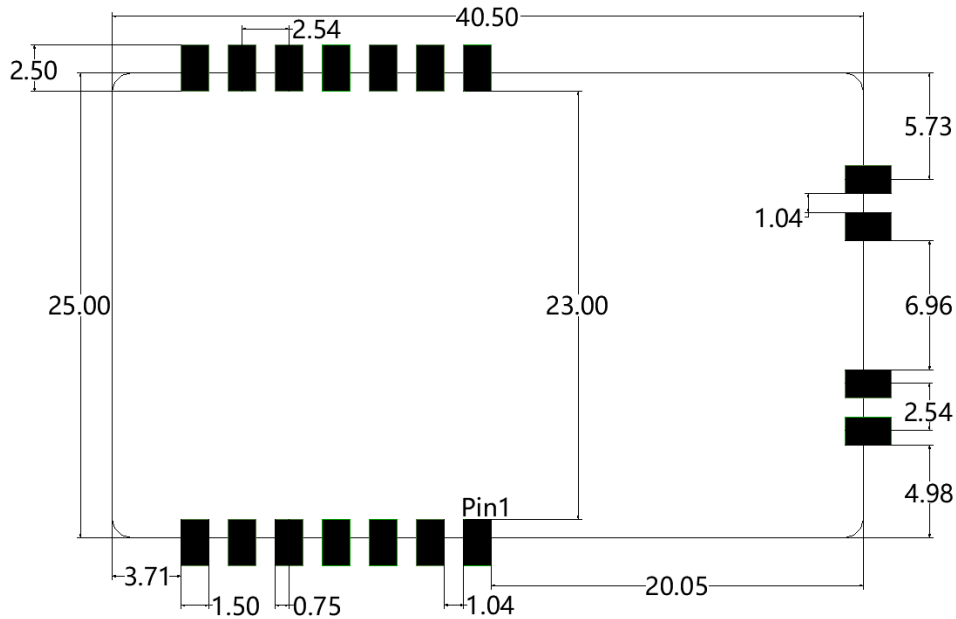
推荐封装(单位:mm,公差:±0.10mm)
